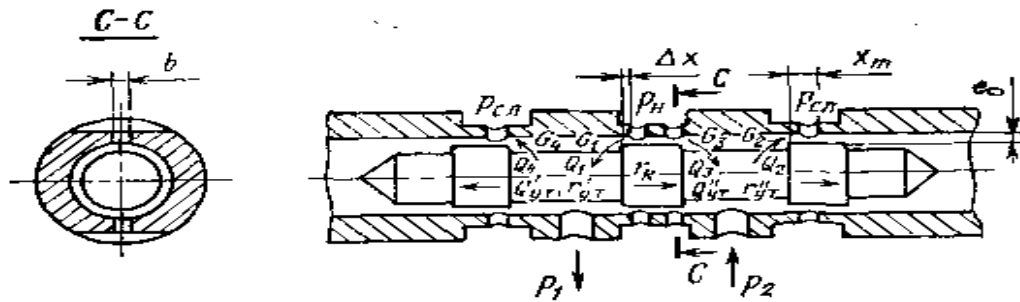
Конструктивная схема четырехщелевого цилиндрического золотника
